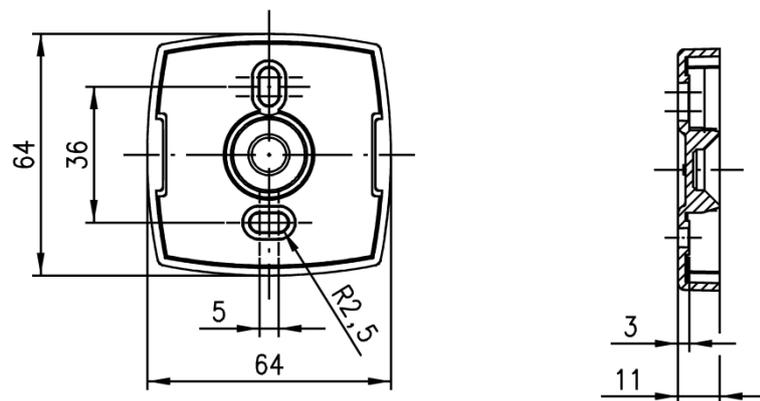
Draufsicht und Querschnitt von der Adapterplatte
